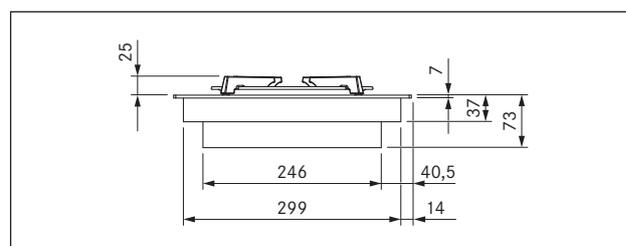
Dimensões do aparelho CKG, vista frontal
